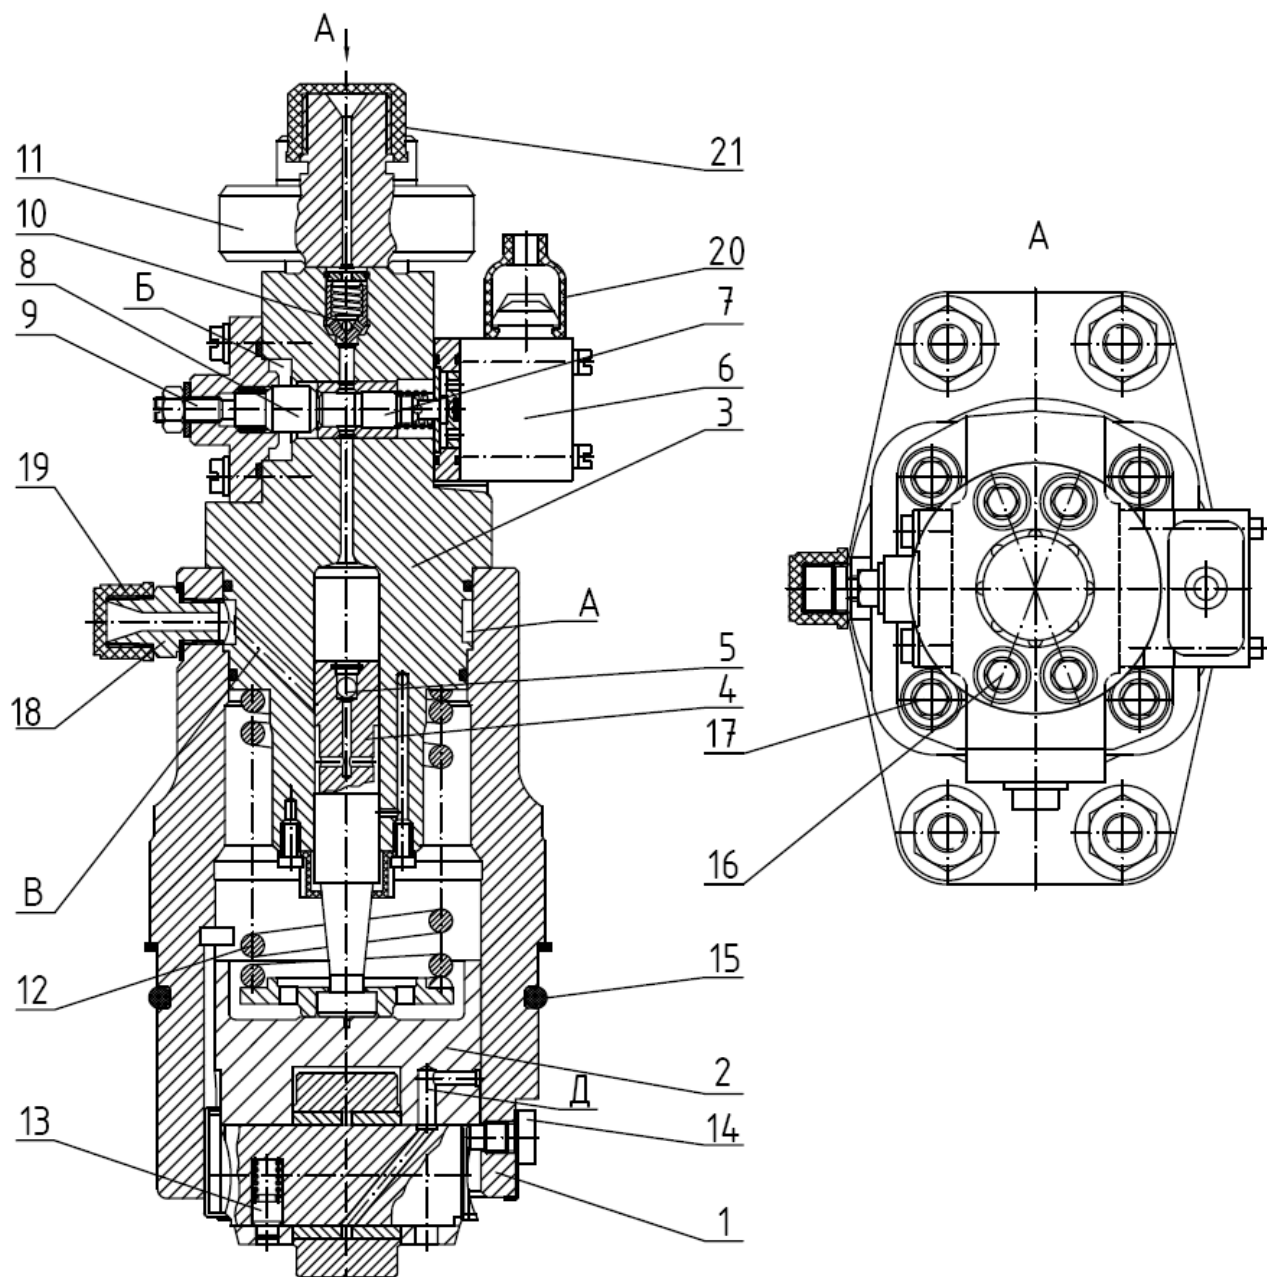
Конструкція модернізованого паливного насосу дизеля MAN 6L40/54: 1 – корпус; 2 – роликовий штовхач; 3 – втулка; 4 – плунжер; 5 – зворотний клапан; 6 – керуючий електромагнітний клапан; 7 – затвор; 8 – упор; 9 – регулювальний гвинт; 10 – нагнітальний клапан; 11 – штуцер високого тиску палива; 12 – пружина; 13 – підпружинений штифт; 14 – гвинт; 15 – ущільнююче кільце; 16 – гвинт; 17 – гвинт; 18 – штуцер низького тиску; 19, 20 і 21 – захисні ковпачки
